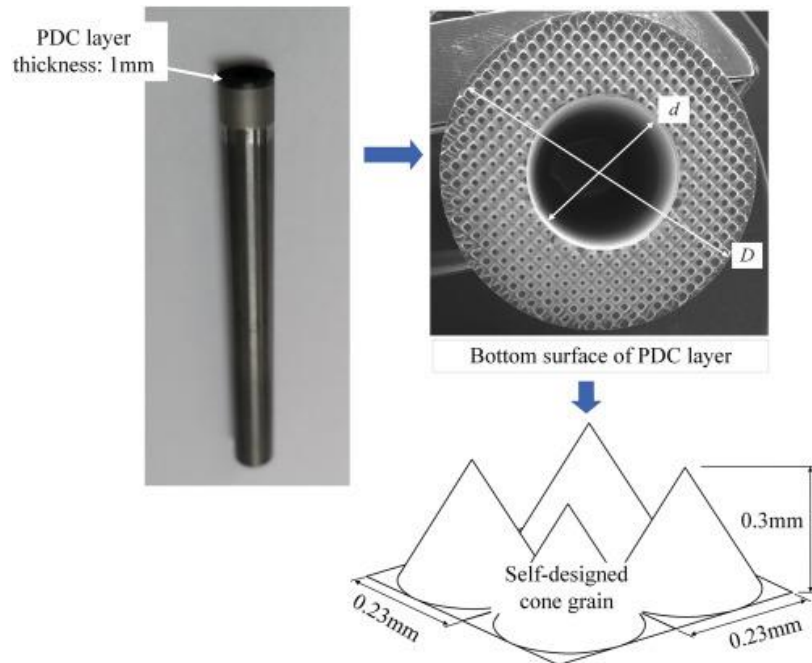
Схема конструкції інструмента і конусного зерна фрезерно-шліфувального інструмента PDC [9]
